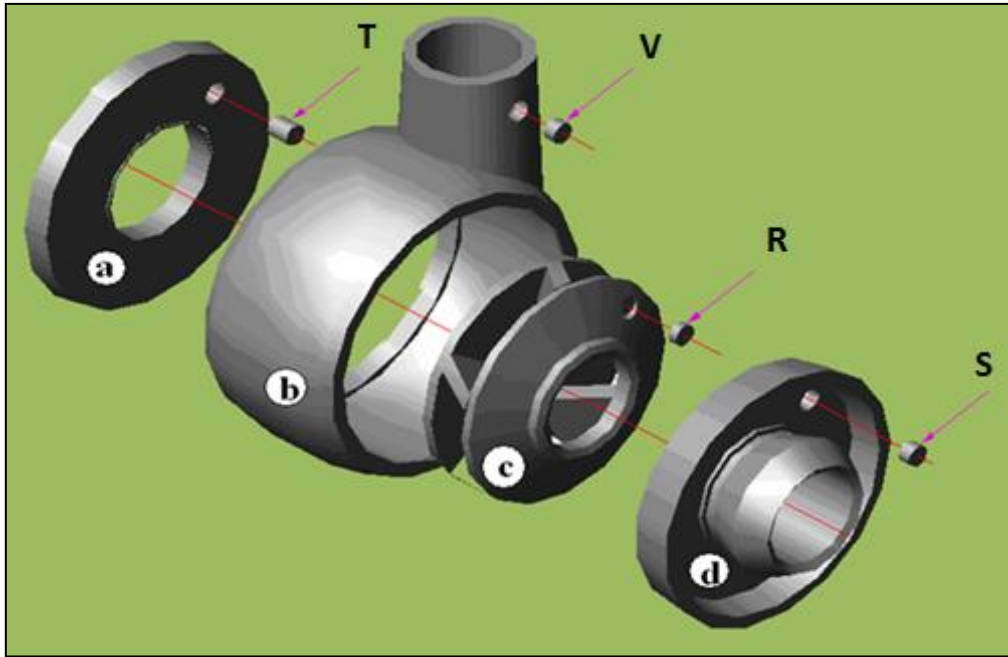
Vista explodida bomba de polpa indicando seus componentes e locais da retirada das amostras: a) Tampa da descarga; b) Voluta; c) Rotor; d) Tampa da sucção.
